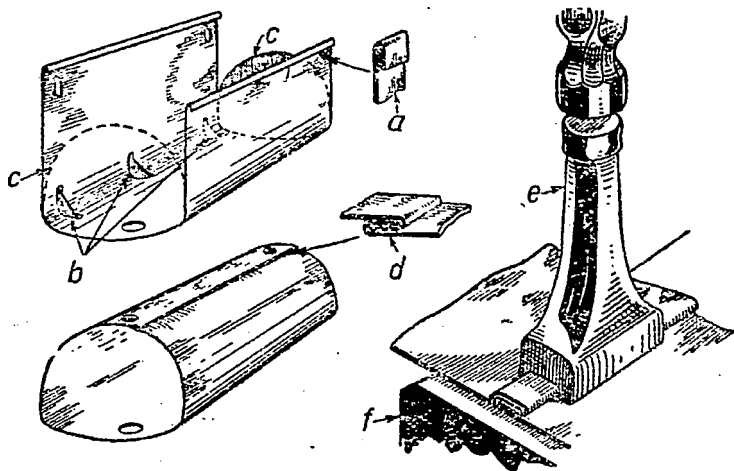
Изготовление шва в двойную нахлестку: *a*—загиб края листа; *b*—усиленные угольники; *c*—стенки бака; *d*—соединительный шов.
